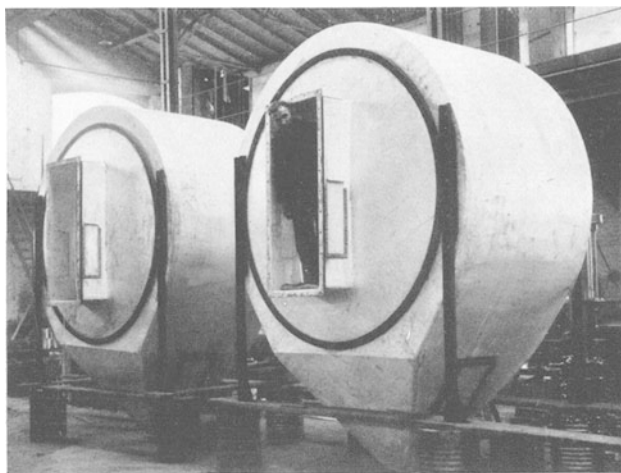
Geschweißte Ausfallgehäuse.
